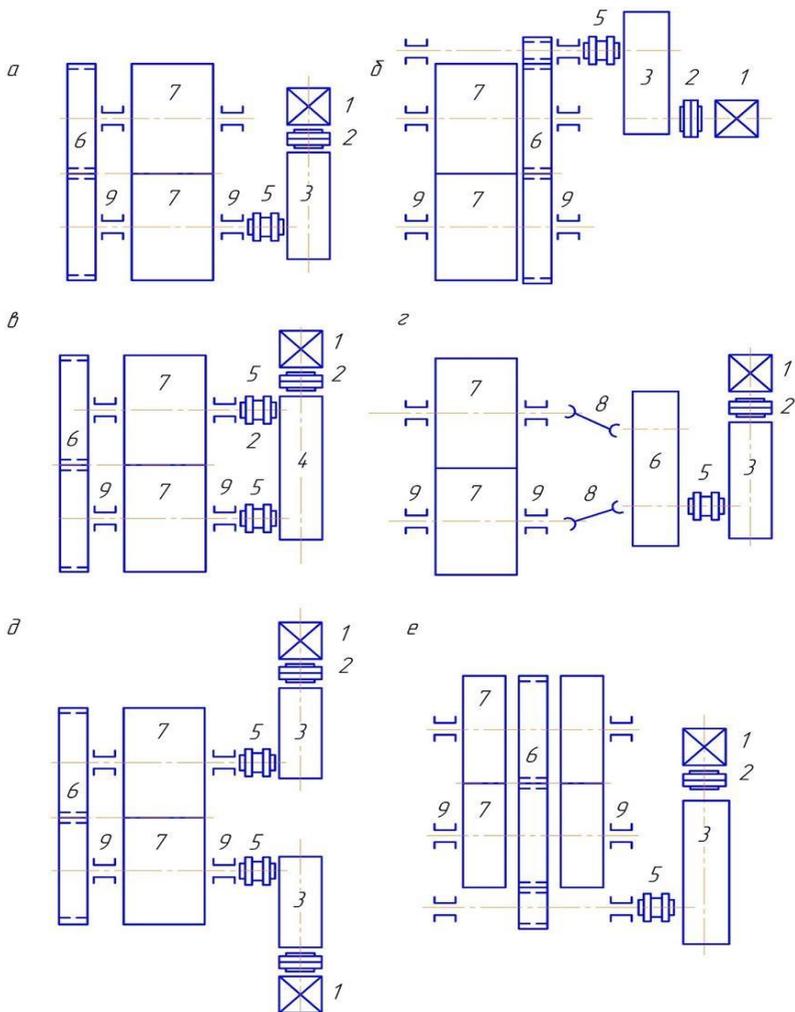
Схемы компоновочных решений валковых прессов: 1 – электродвигатель; 2 – муфта соединения электродвигателя с редуктором; 3 – редуктор; 4 – раздаточный редуктор; 5 – муфта соединения вала с редуктором; 6 – синхронизирующая передача (открытого или закрытого типа); 7 – валки со сменными бандажами или сегментами; 8 – шпindel; 9 – подшипниковые опоры валков.
